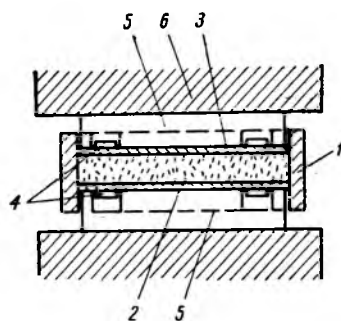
Схема прессования плиты в пресс-форме: 1 — стенки пресс-формы; 2 — дно; 3 — крышка; 4 — щелевидные отверстия; 5 — вспомогательная прокладка из текстолита; 6 — металлические плиты пресса
